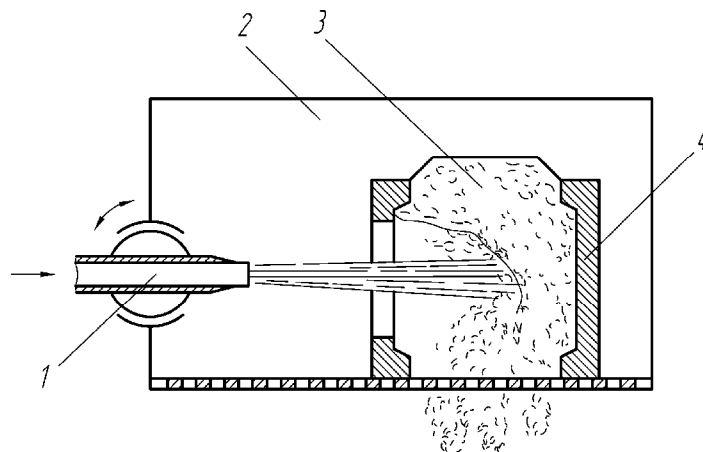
Схема удаления стержня из отливки в гидравлической камере:
